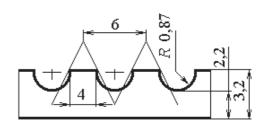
Размеры образца в зоне дна резьбы M64x6
